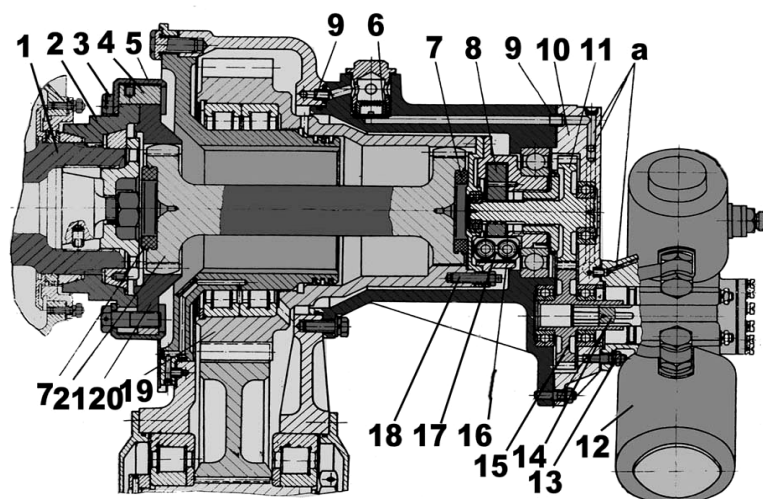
Привод к компрессору: 1 – носок коленчатого вала двигателя; 2 – муфта; 3 – болт крепления муфт; 4 – сухарь; 5 – скоба; 6 – предохранительный фильтр; 7 – резиновые буфера; 8 – ведомая муфта; 9 – переходные втулки; 10 – картер редуктора; 11 – ведущая шестерня редуктора; 12 – компрессор; 13 – детали крепления компрессора; 14 – хвостовик компрессора; 15 – ведомая шестерня редуктора; 16 – ведущая муфта; 17 – подпружиненные вкладыши; 18 – болты крепления муфты; 19 – ведущая шестерня входного редуктора; 20 – зубчатая муфта; 21 – зубчатый вал; а – каналы
